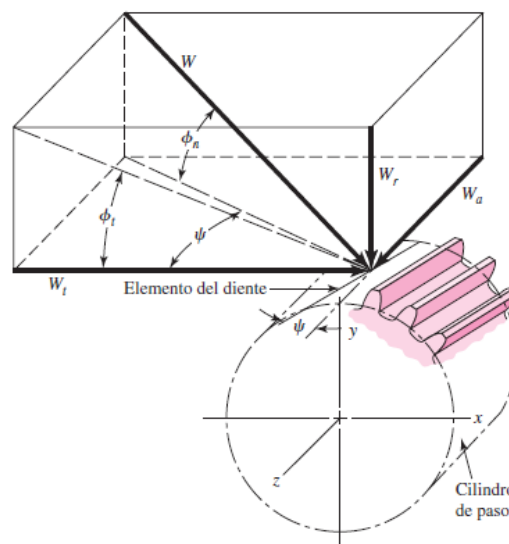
Fuerzas que actúan en los dientes de un engrane helicoidal [2].
